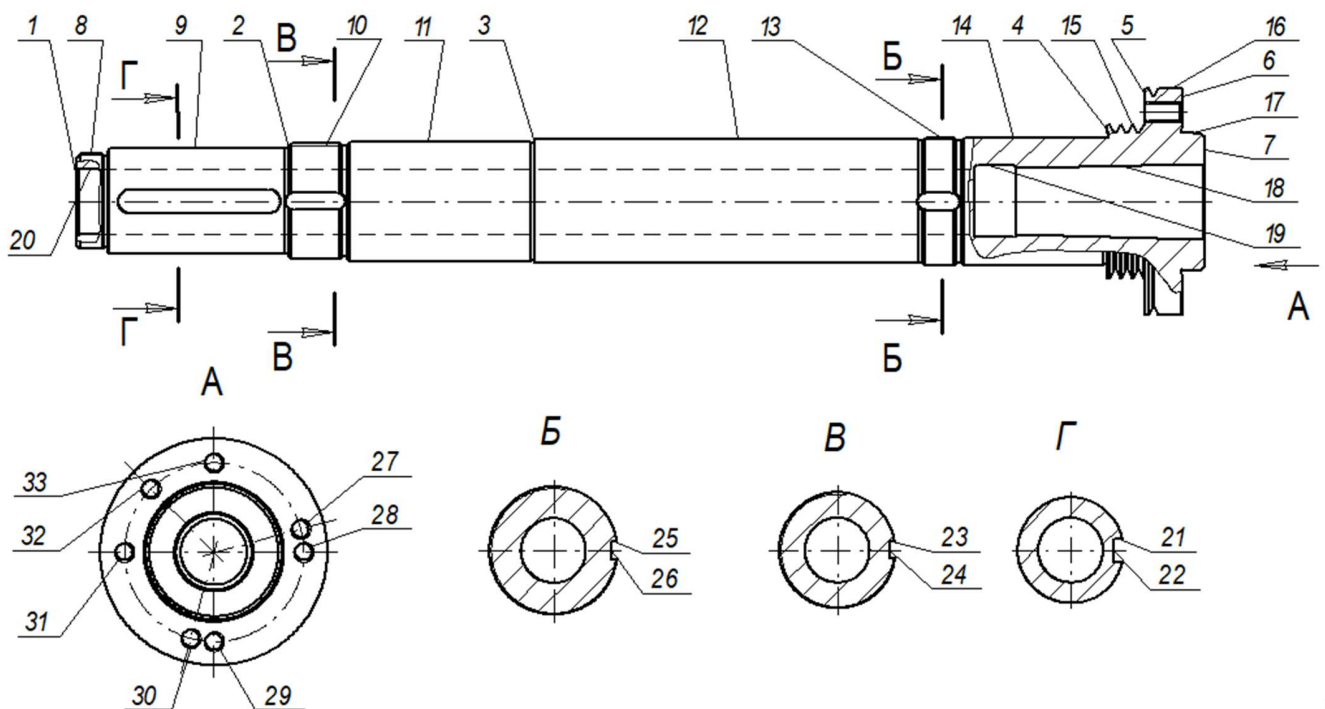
Позначення поверхонь шпинделя токарного верстату
